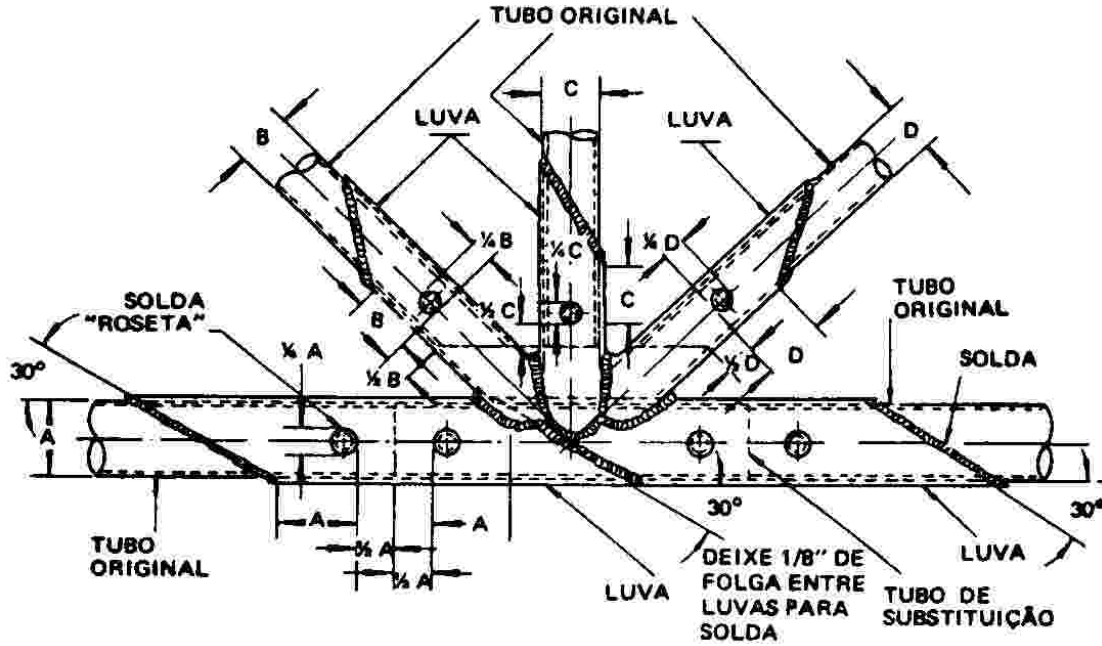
Reparo de Tubo num Nó por Luvas Externas Soldadas
